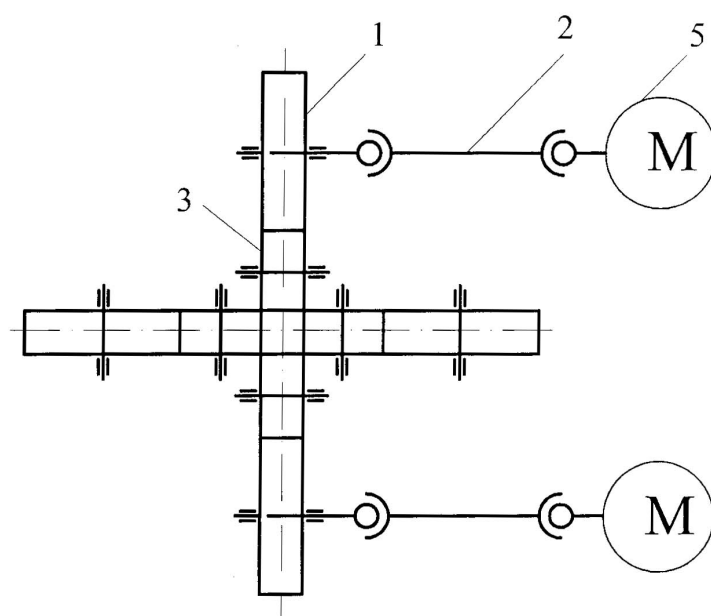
Главная линия клетки с четырехвалковым калибром с приводными опорными валками
